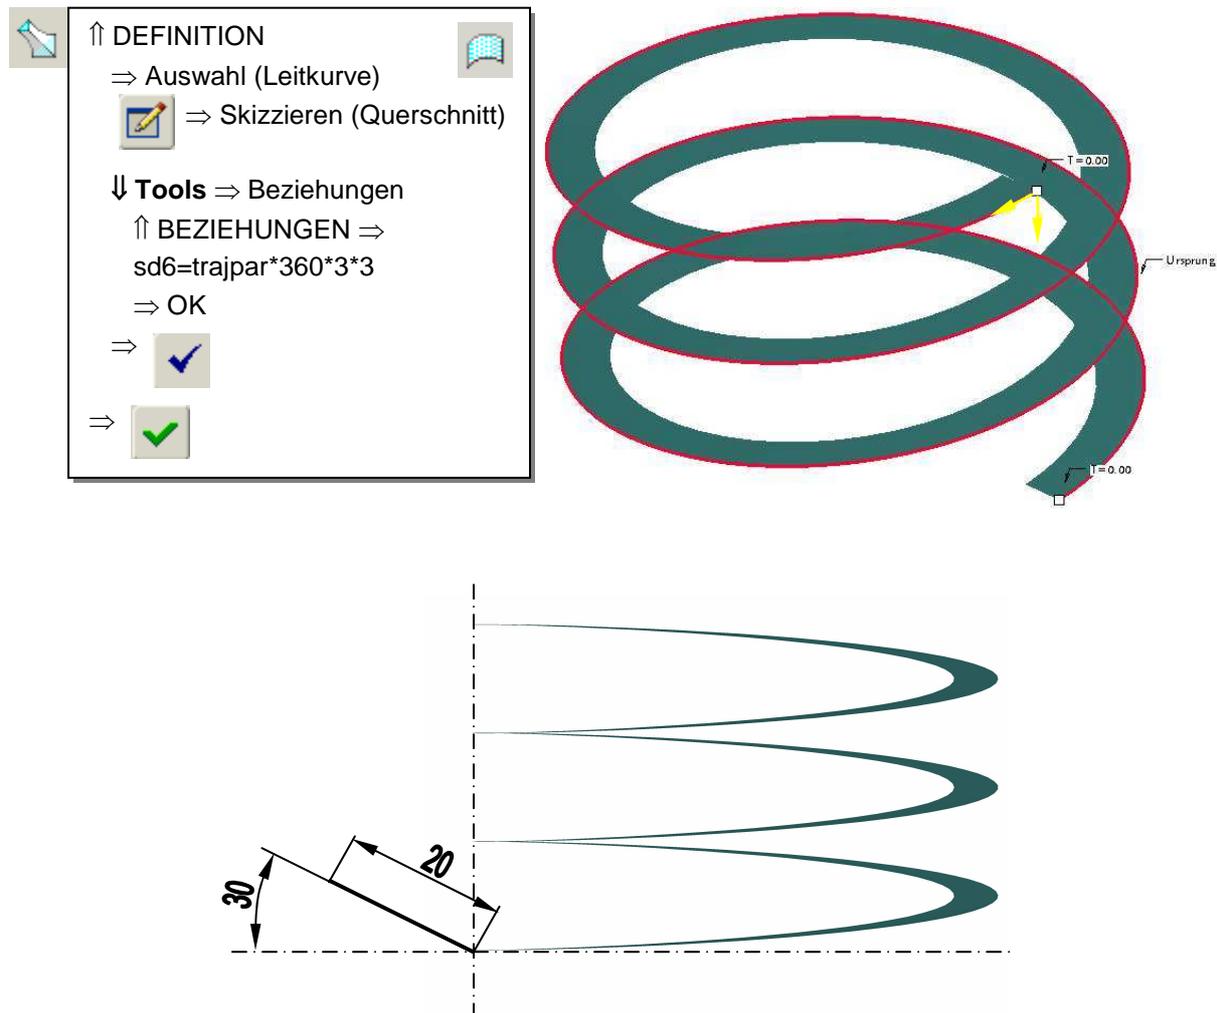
Erzeugung einer gewundenen Spiralfäche
